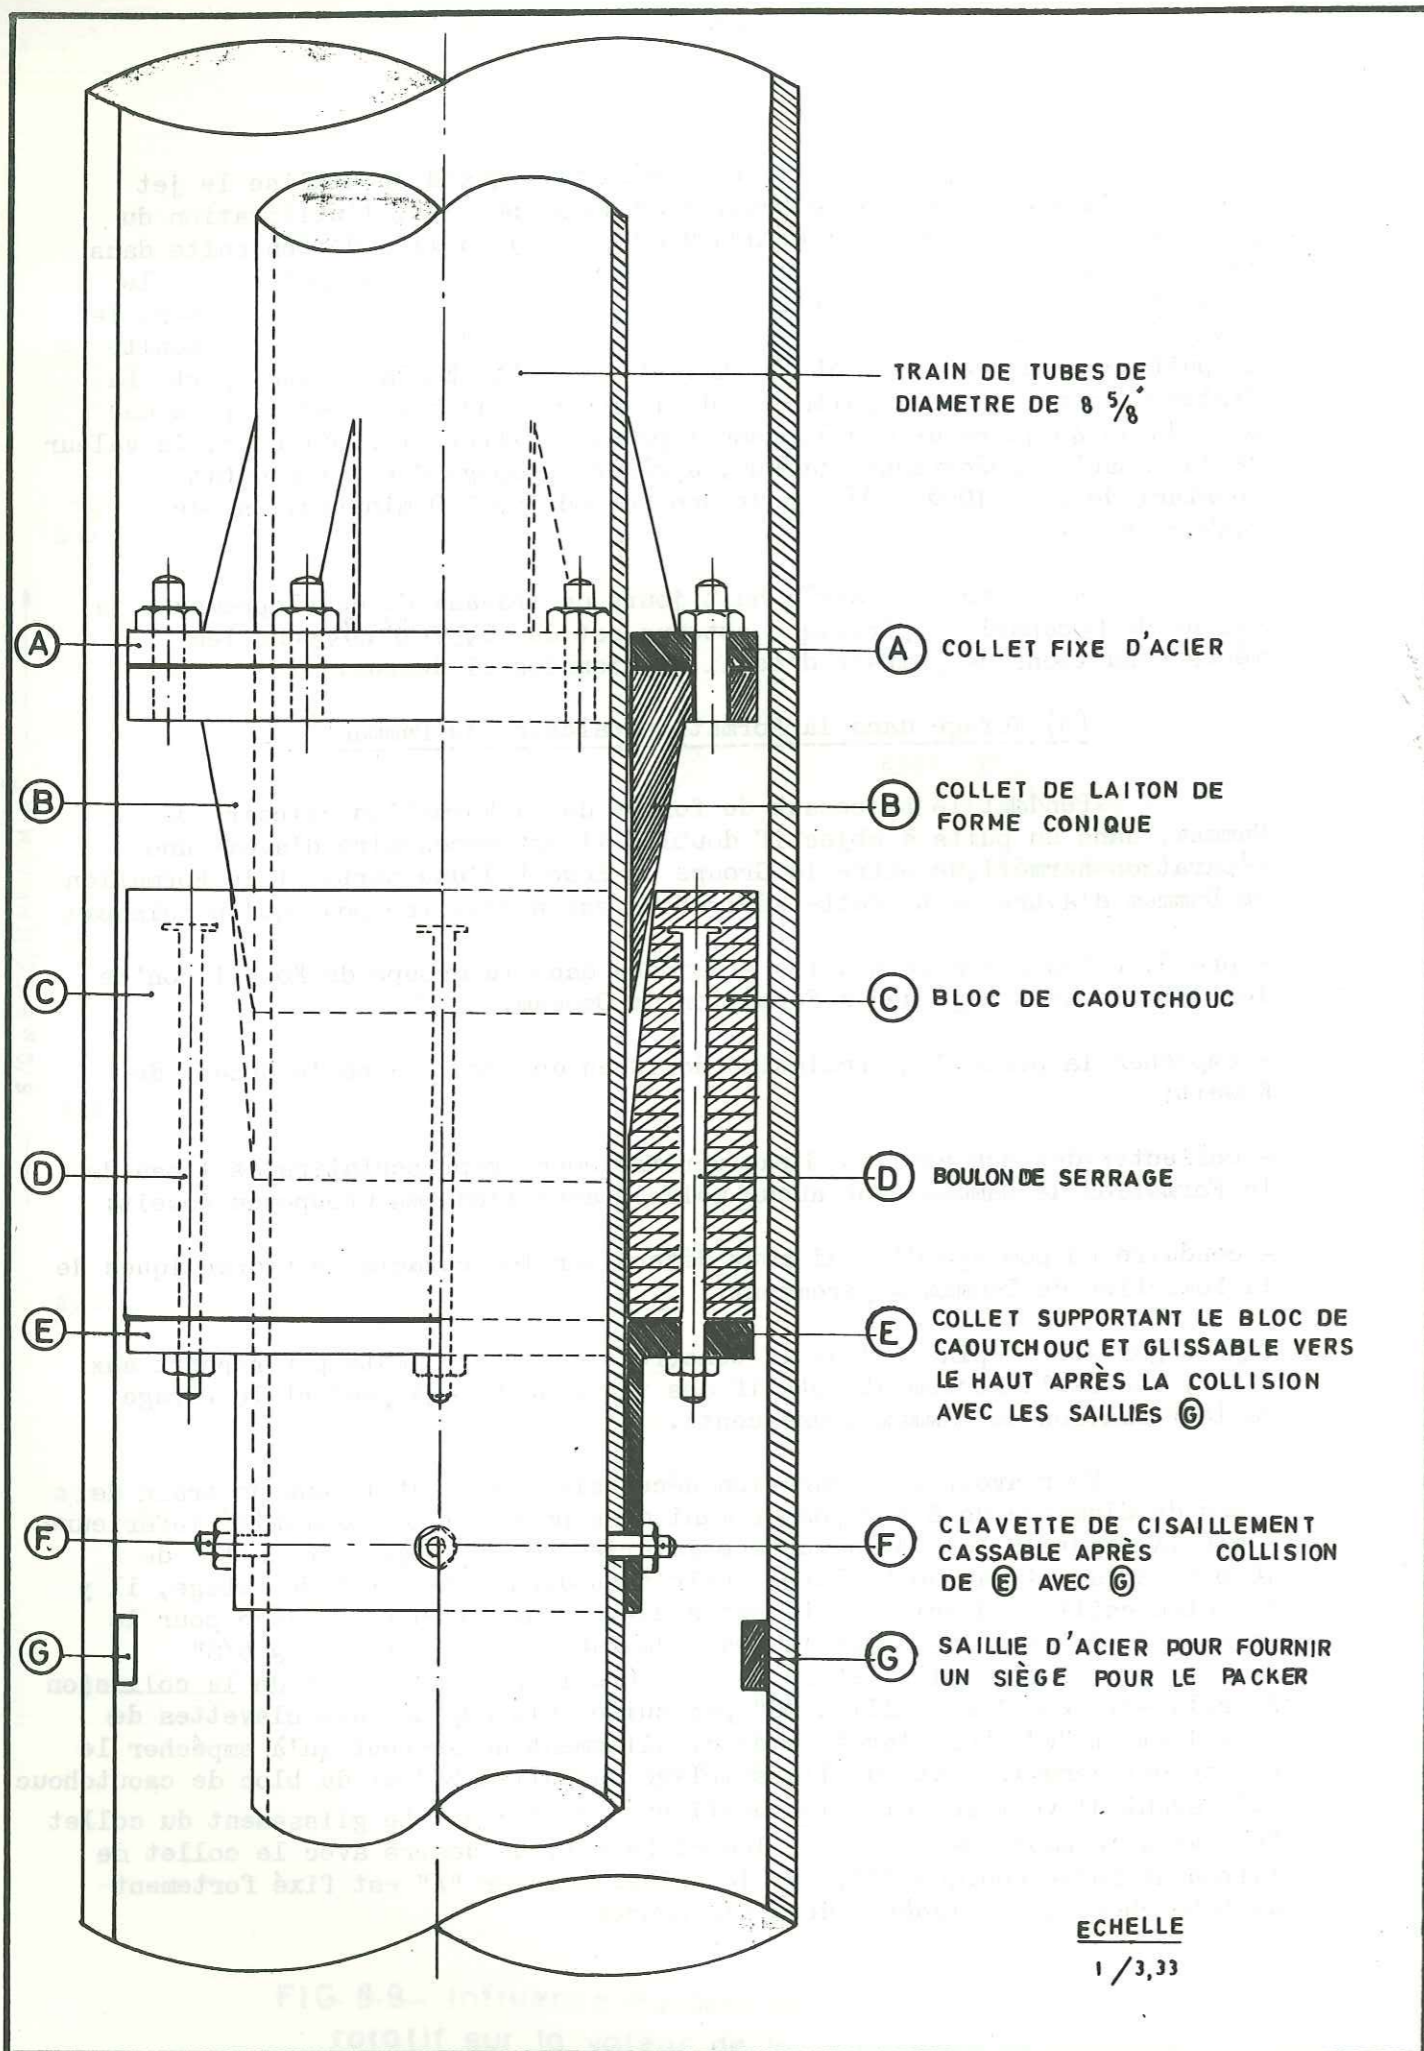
Dessin du packer utilisé pour la séparation des aquifères (D'après S.E.S., 1979)
